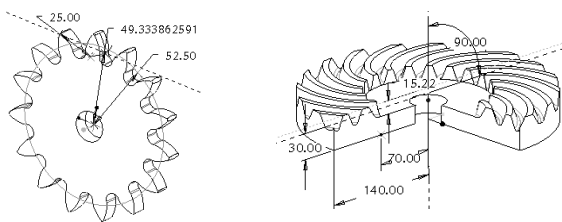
Основні розміри циліндричного (а) та конічного (б) коліс
